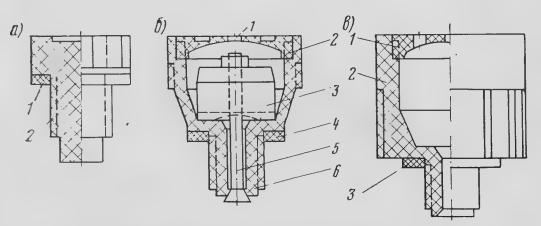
Конструкция пробок аккумуляторных батарей: а— глухая пробка для аккумуляторных батарей 12-А и 12-САМ; 1— резиновая шайба; 2— корпус пробки;
